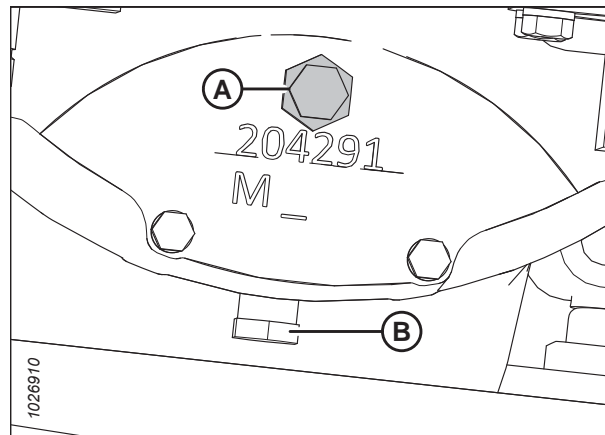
Пробка отверстия для слива масла из редуктора
